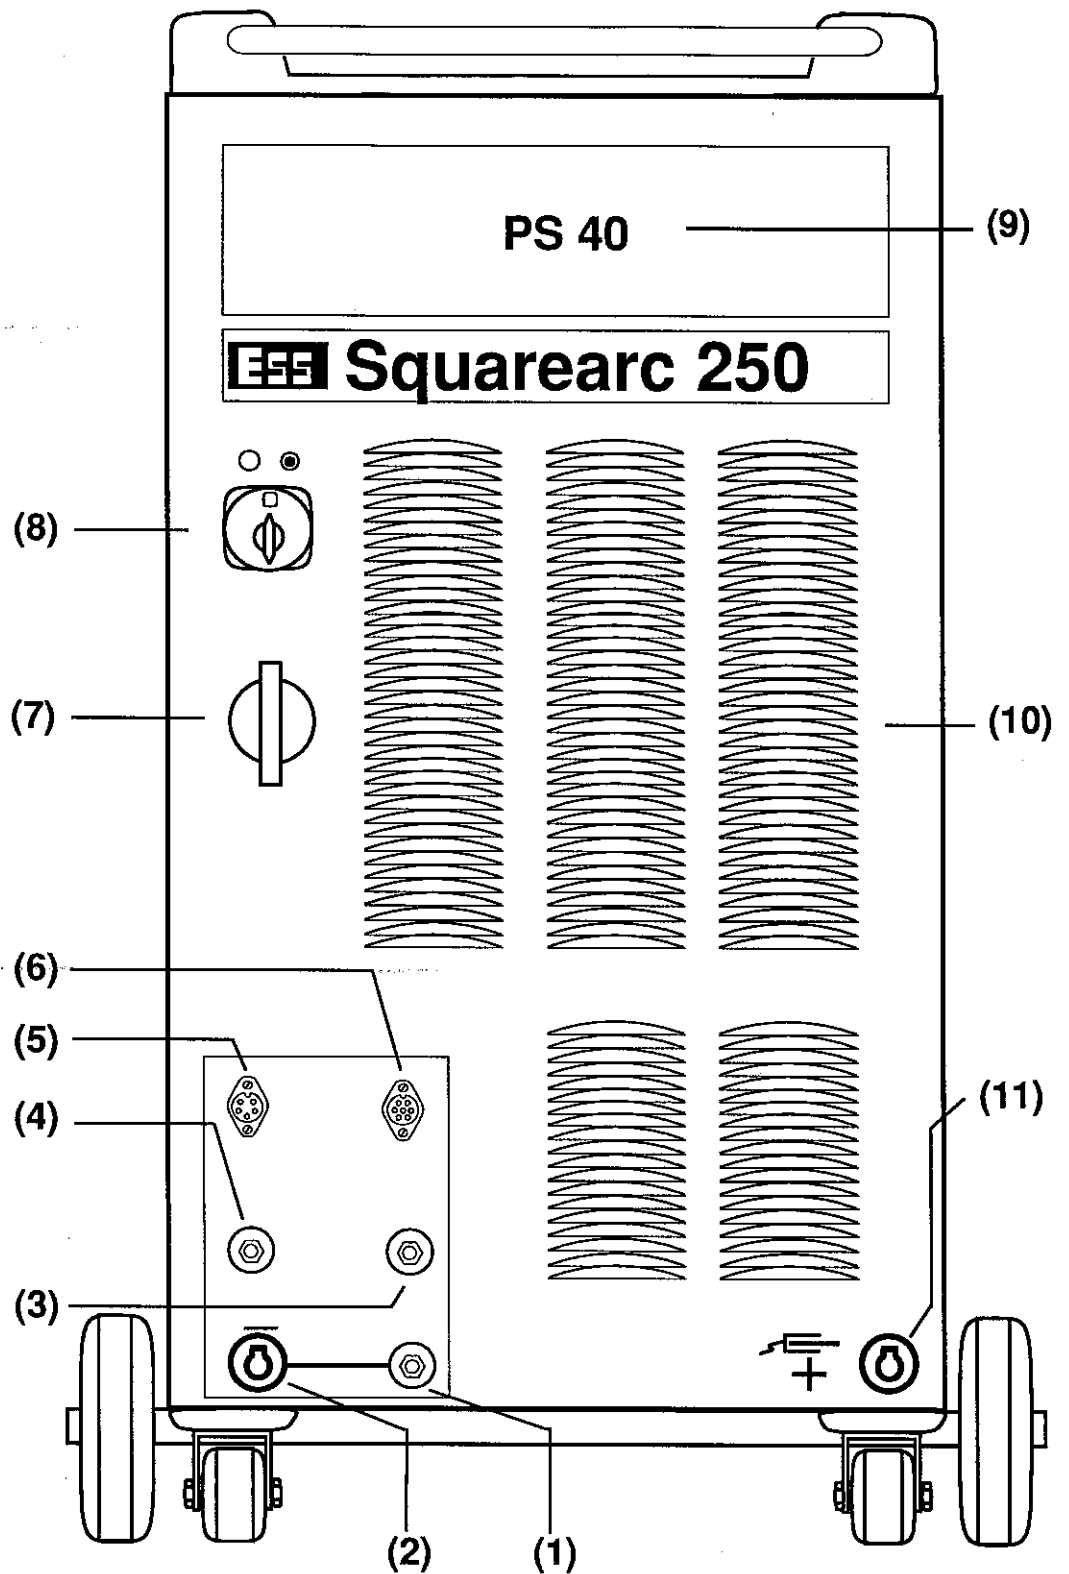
WIG-Schweißstromquelle, Typ Squarearc 250, Vorderansicht
